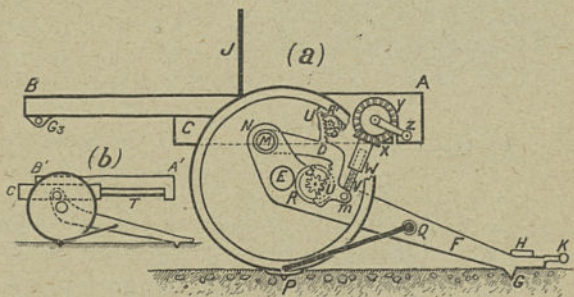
Ensemble de la pièce de 75. — (a) avant le tir ;
